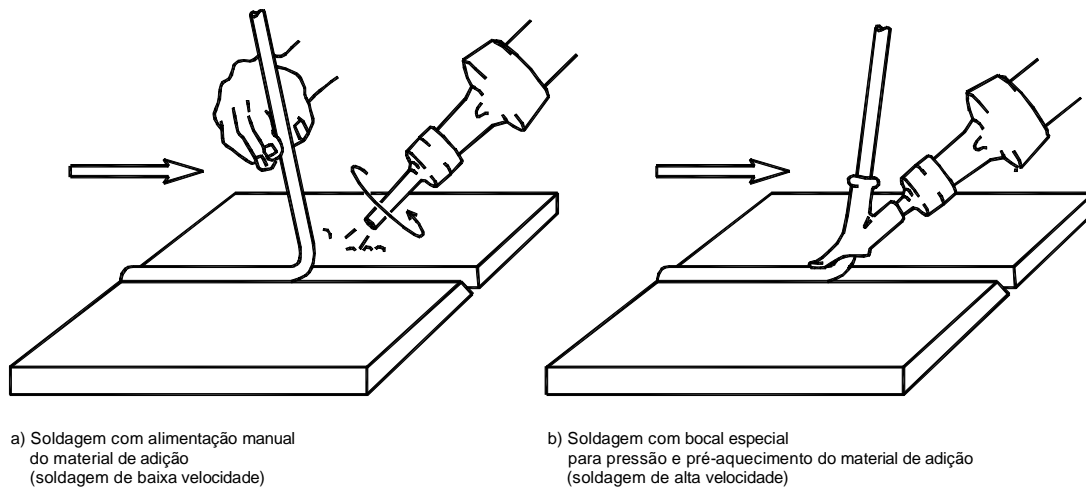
Soldagem por ar quente com alimentação manual do material de adição (a) e com uso de bocal especial para soldagem rápida (b)
